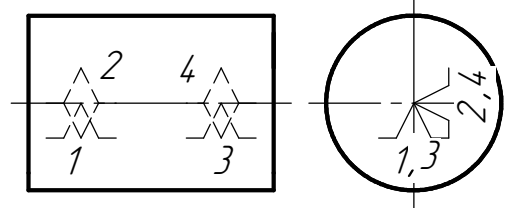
Теоретические схемы базирования заготовки по контурным поверхностям (а) и на осевых линиях или точке их пересечения (б)
